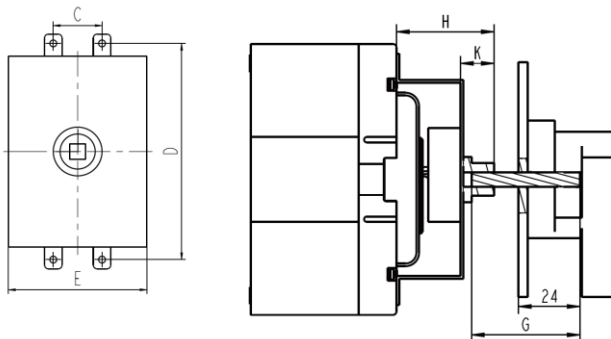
Габаритные и установочные размеры ручки на дверь шкафа РП-300, мм
